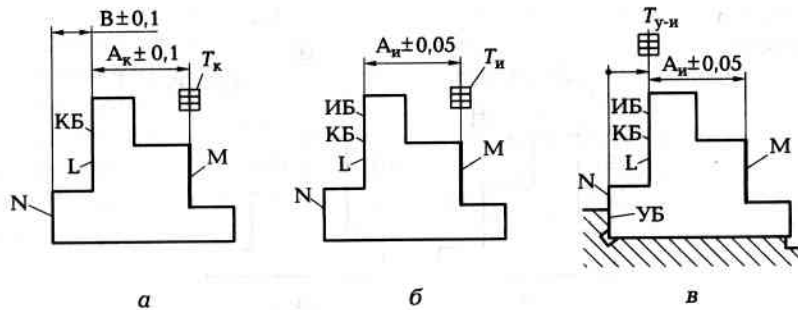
Несовмещение установочной базы и исходной базы (УБ ≠ ИБ)
